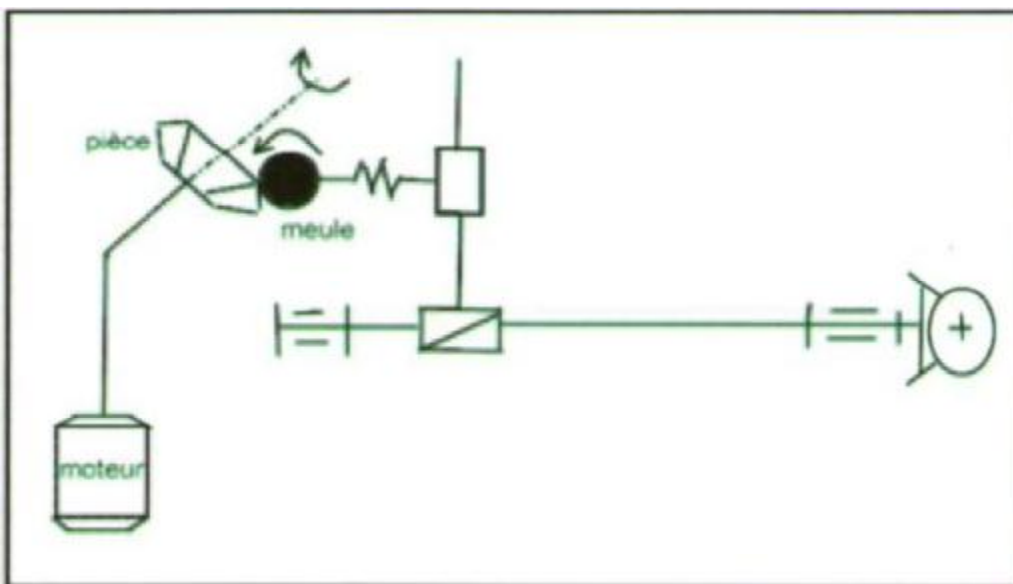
Pour arrête inclinée par à l'axe de la pièce
